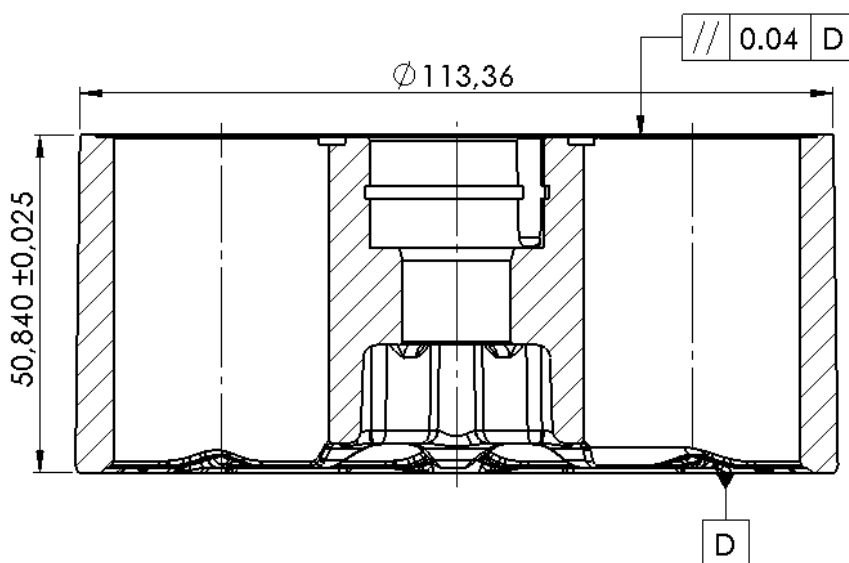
Dimensões e tolerâncias utilizadas do Bloco
